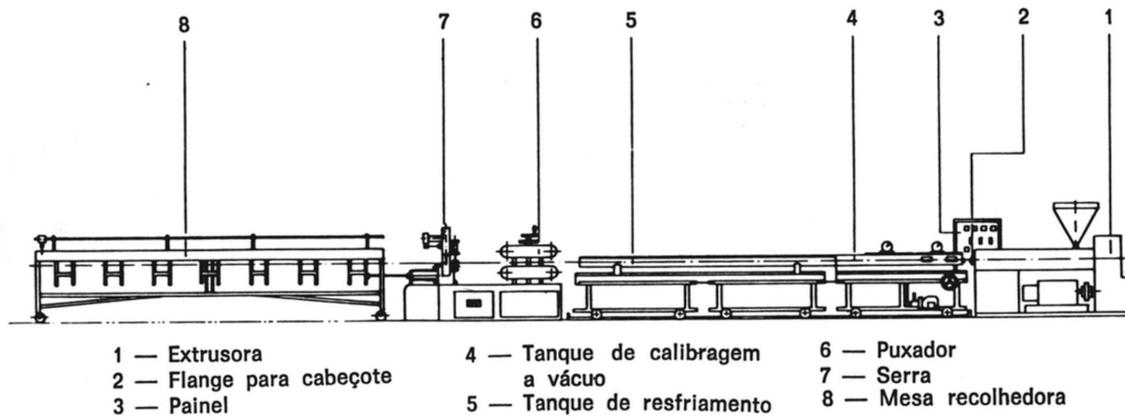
Equipamentos de pós-extrusão na produção de tubos. Um elemento de fixação chamado flange conecta uma extrusora de rosca simples ou dupla à matriz ou ao seu adaptador. Após a extrusão, o tubo, arrastado pelo equipamento puxador (lagartas), passa por um calibrador para tomar sua dimensão final e em seguida por um tanque de resfriamento, para solidificar totalmente e não ser deformado pelos puxadores. Finalmente, o extrudado é cortado no comprimento desejado e recolhido por uma calha.
